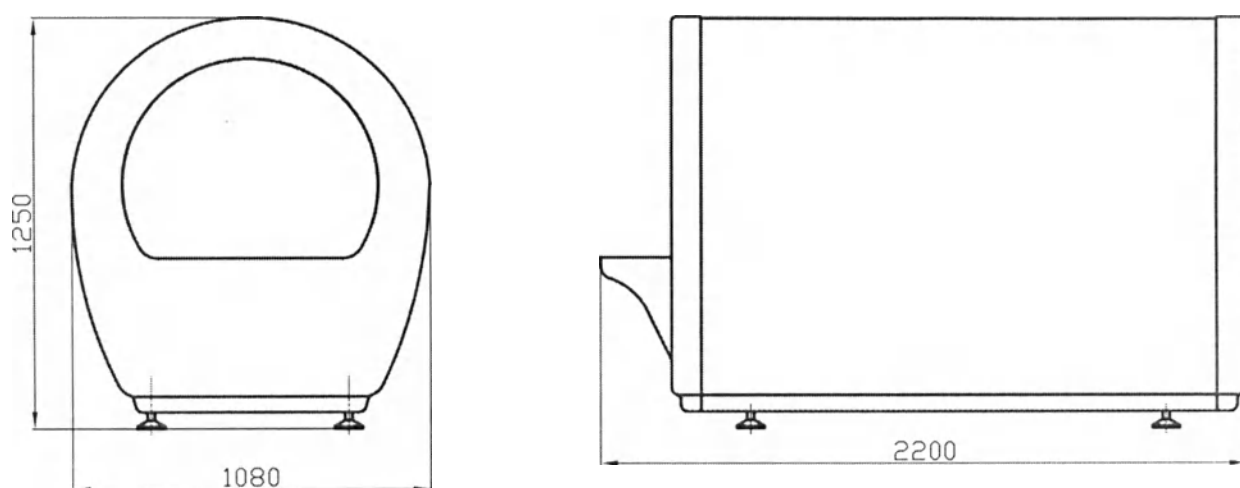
Габаритные размеры лечебной камеры установки исполнения Люкс
